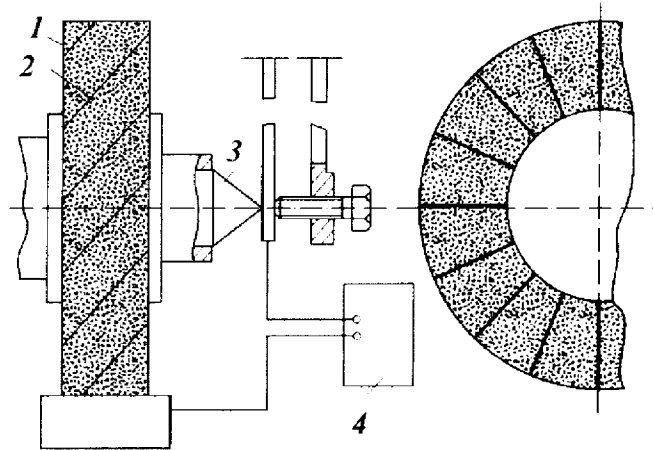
Шлифовальный круг с наклонными витками нихромовой проволоки
